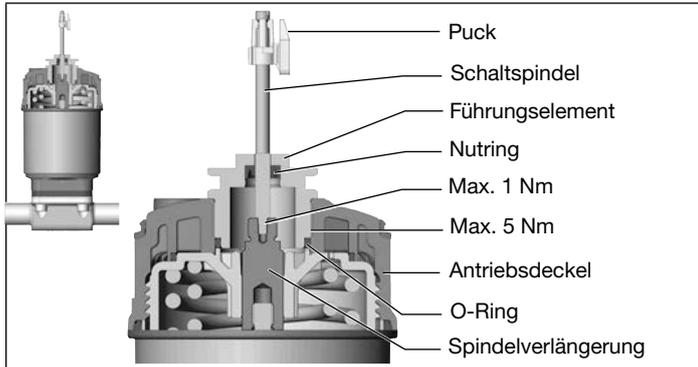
Schaltspindel montieren (2), integrierte Steuerluftführung
